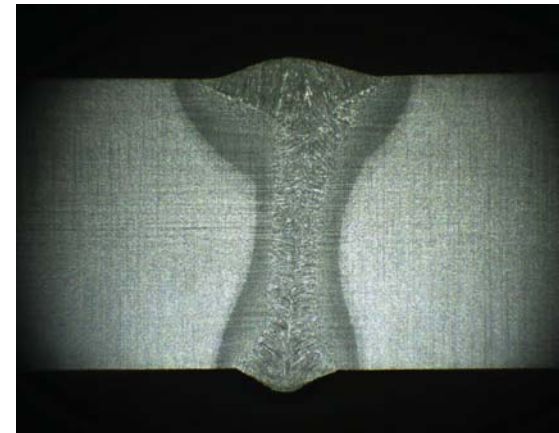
Soudure hybride en bout-à-bout sur acier de 12 mm, aucun chanfrein, une seule passe
